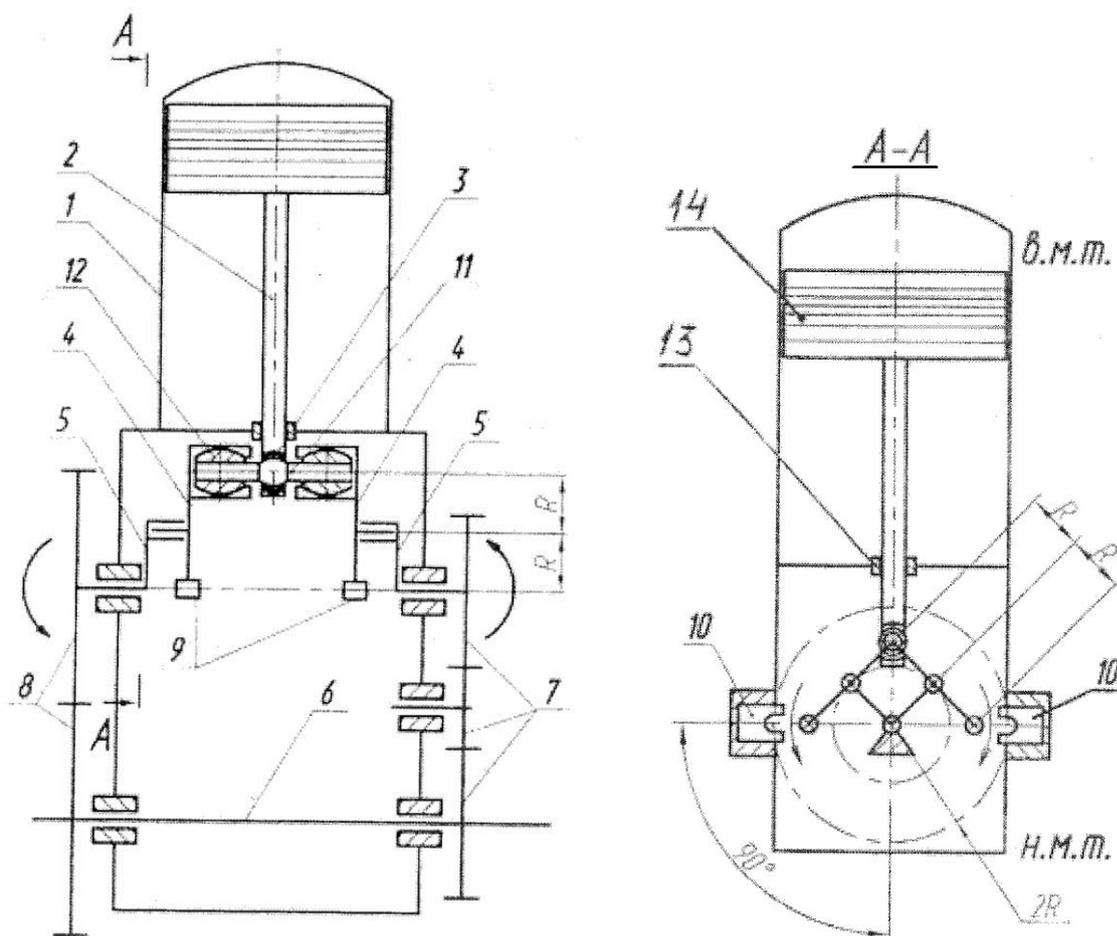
Схема ромбического кривошипно-планетарного поршневого механизма:
